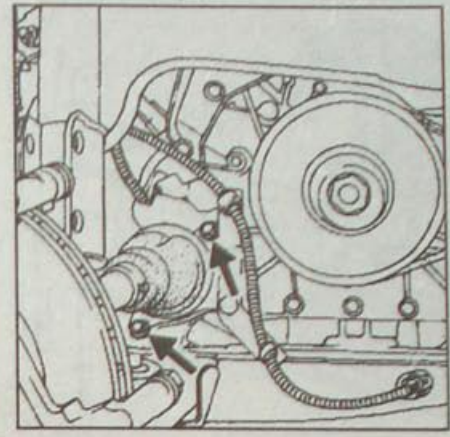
Расположение болтов крепления промежуточной опоры приводного вала в опорном подшипнике коробки передач РК1
